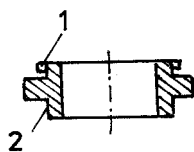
Bucșă de îmbinare: 1- capătul care se montează în pinionul mic; 2- capătul care se montează în pinionul mare
